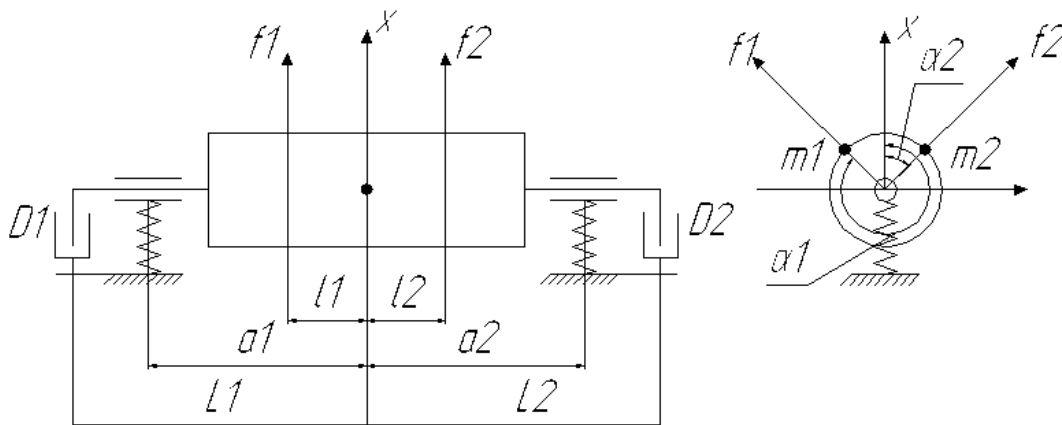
ротор, установленный в упругих опорах балансировочного станка
